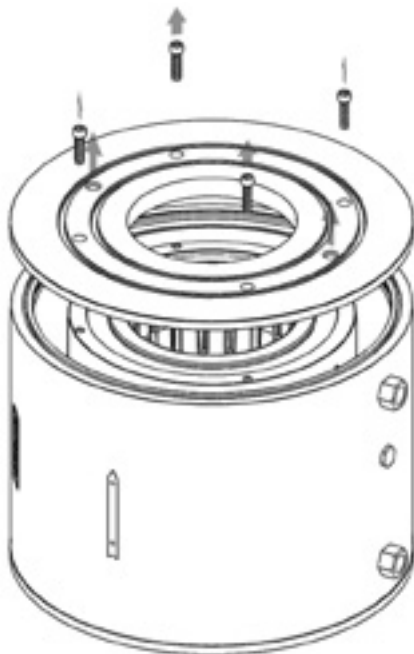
Entfernen Sie die Abdeckplatte am Austritt.
